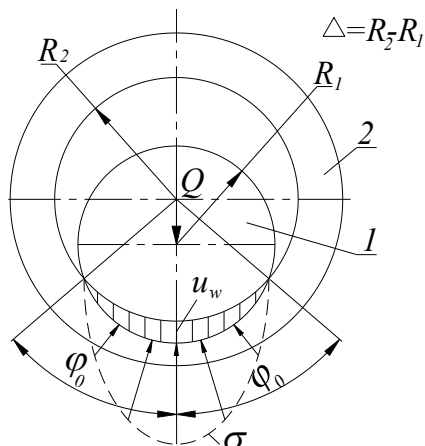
Розрахункова схема підшипника ковзання з прямою парою тертя
